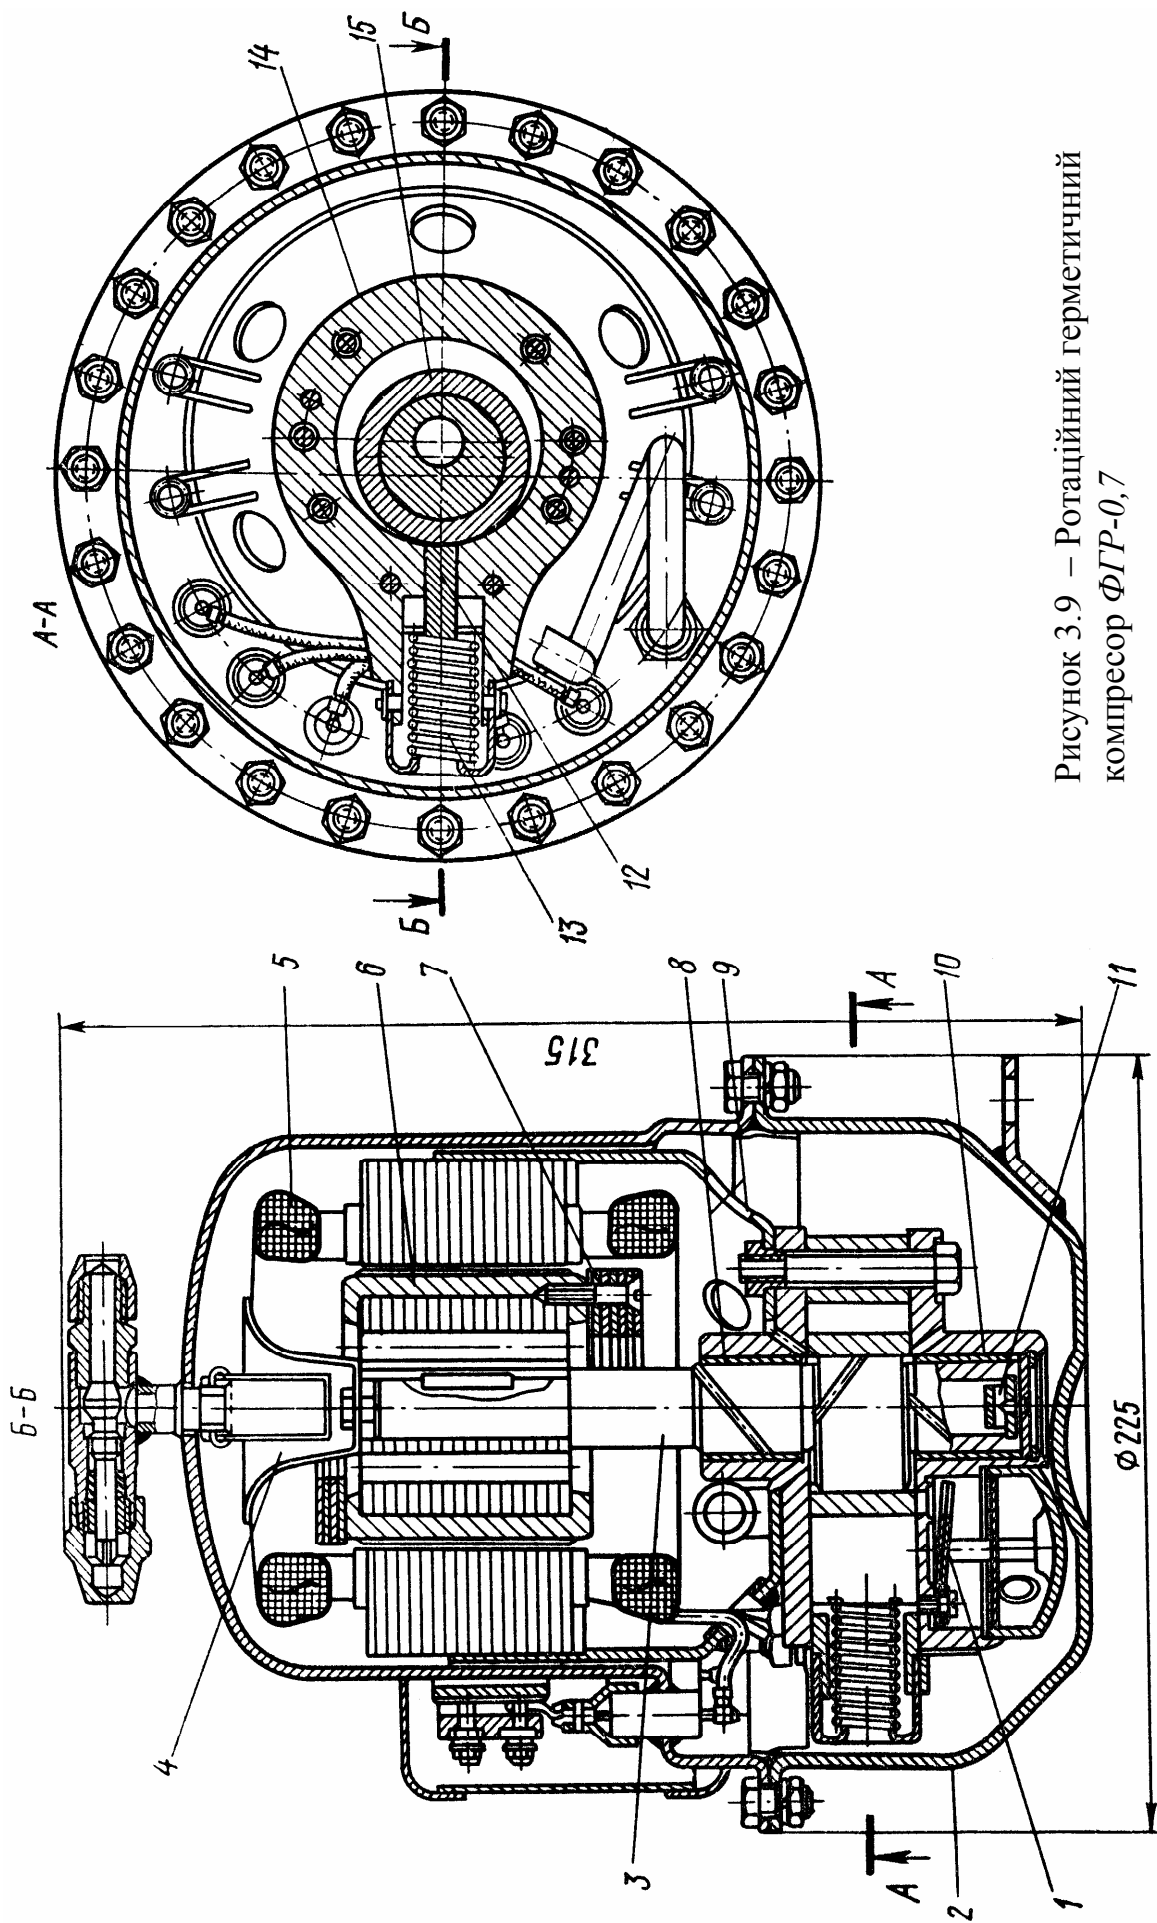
Ротаци́нный герметичный компрессор ФГР-0,7
